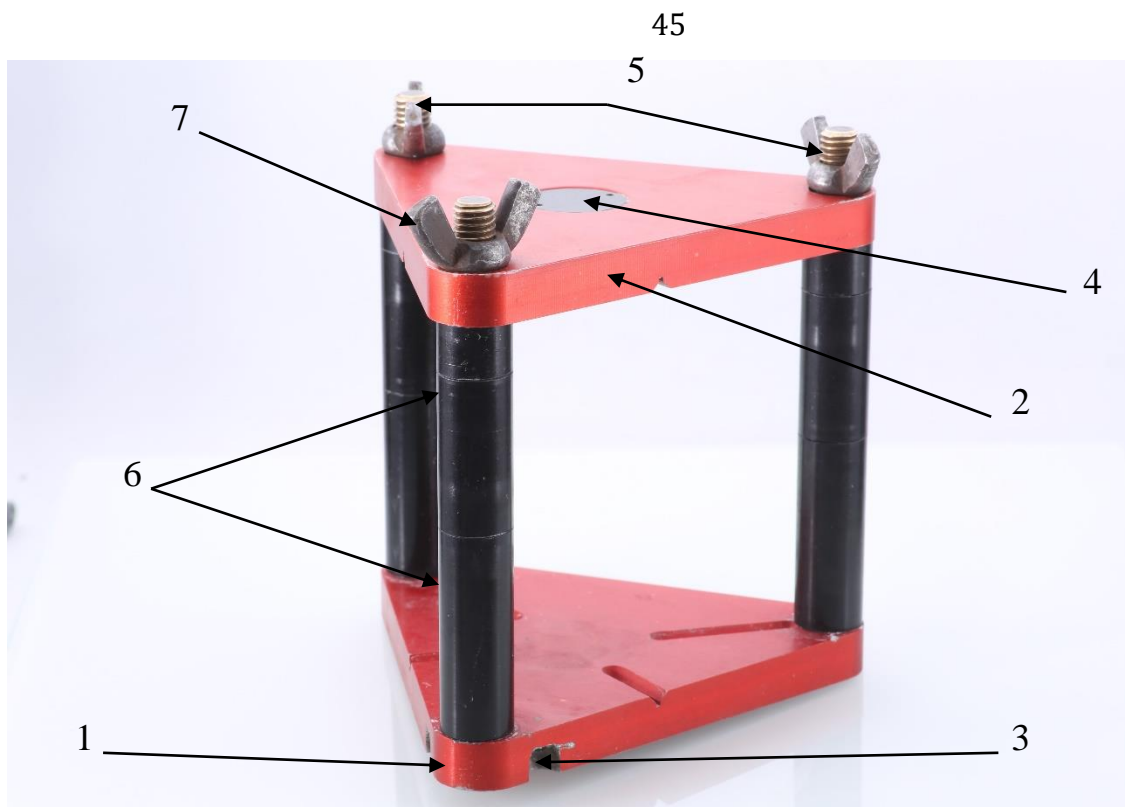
Устройство для изготовления зубных протезов (вертикалятор «Кравеца»)
